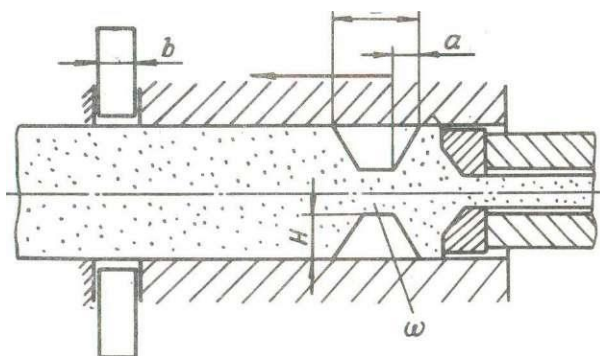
Схема подачи очередной порции заготовки в контейнер пресса
